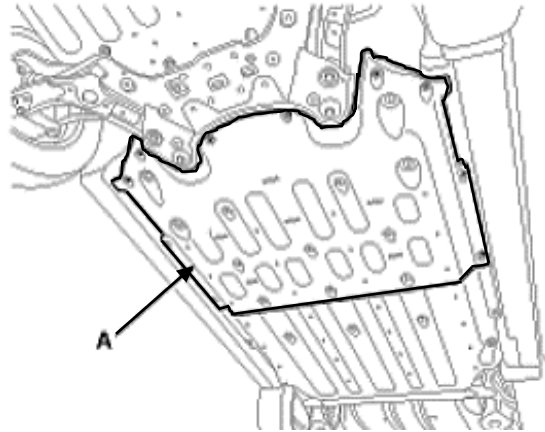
Desmontaje de cubierta inferior delantera de la batería de alta tensión
